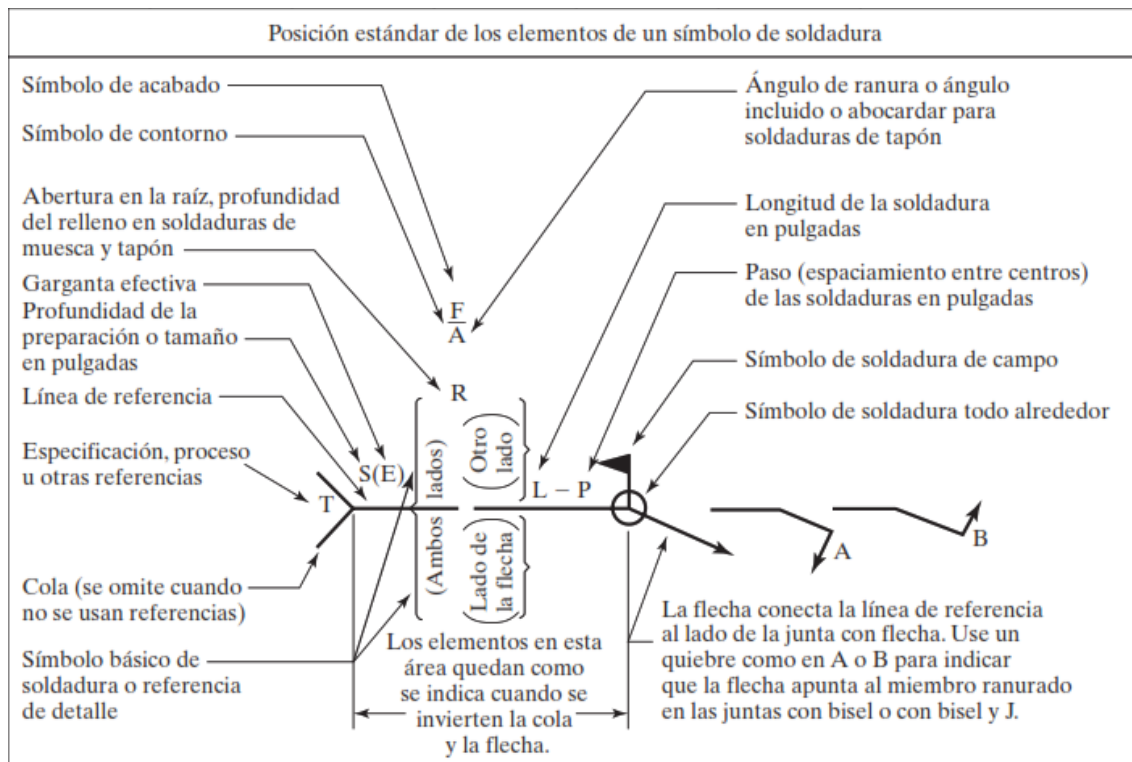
Notación estándar de soldadura (McCormac & Csernak, 2012)
